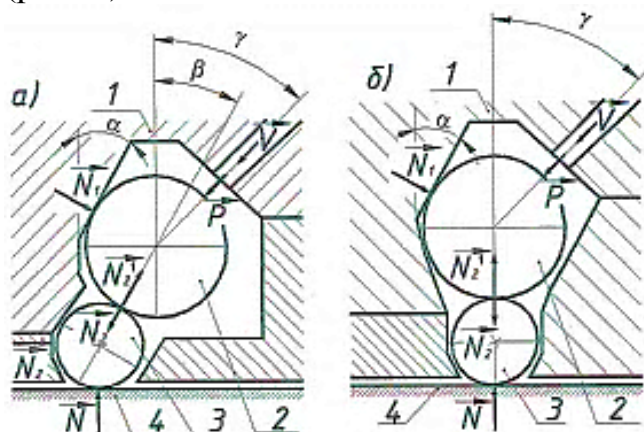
Принципиальные схемы воздействия сил на шары инструмента и обрабатываемую поверхность: а – случай А,  $\beta \neq 0$ ; б – случай В,  $\beta=0$ ; 1 – направляющая поверхность; 2 – шар-ударник; 3 – шар-боек; 4 – обрабатываемая поверхность
